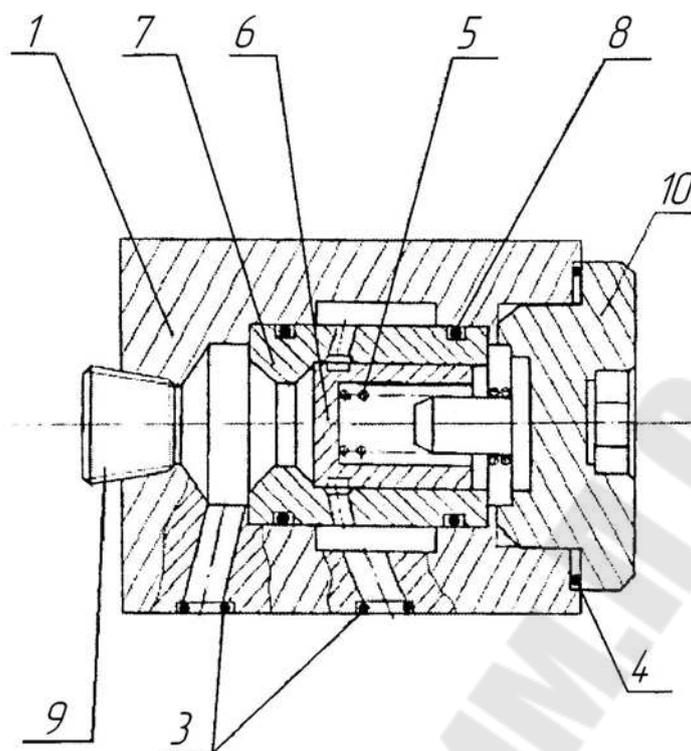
Блок присоединительный клапана обратного типа БПВ-...*КО
